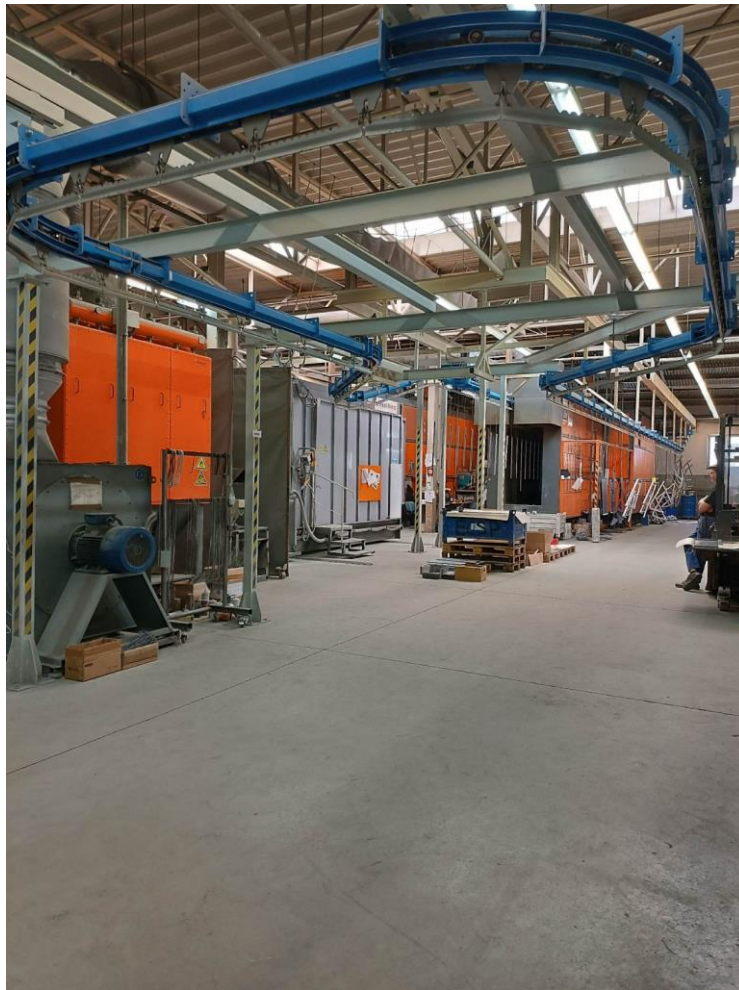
Layout oddělení lakovny (interní zdroj)
